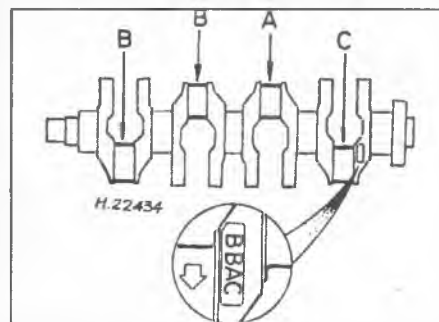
Буквы размерной группы шатунной шейки коленчатого вала – бензиновый двигатель
